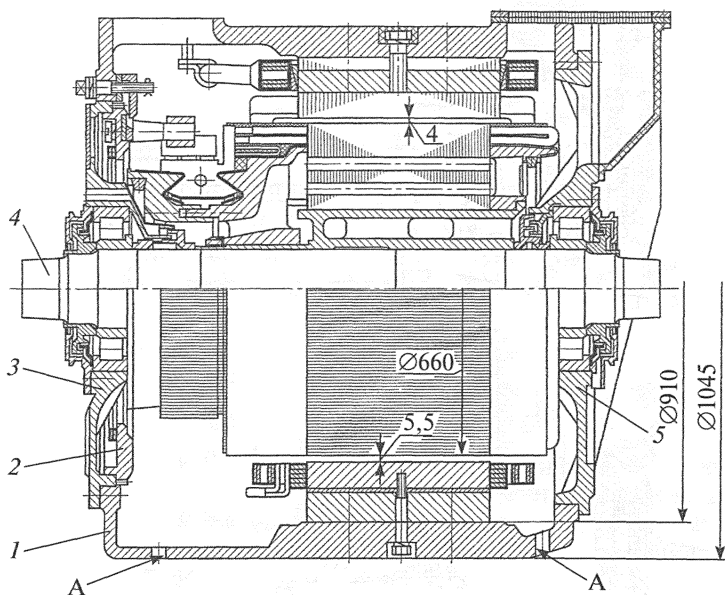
Продольный разрез тягового двигателя НБ-514 Б:
